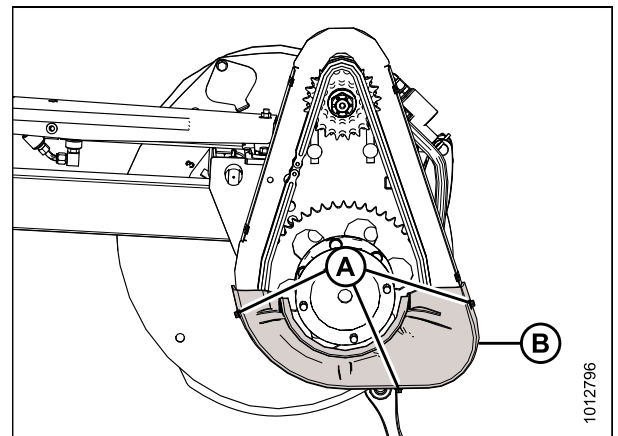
Cubierta de mando inferior (cubierta superior retirada)
